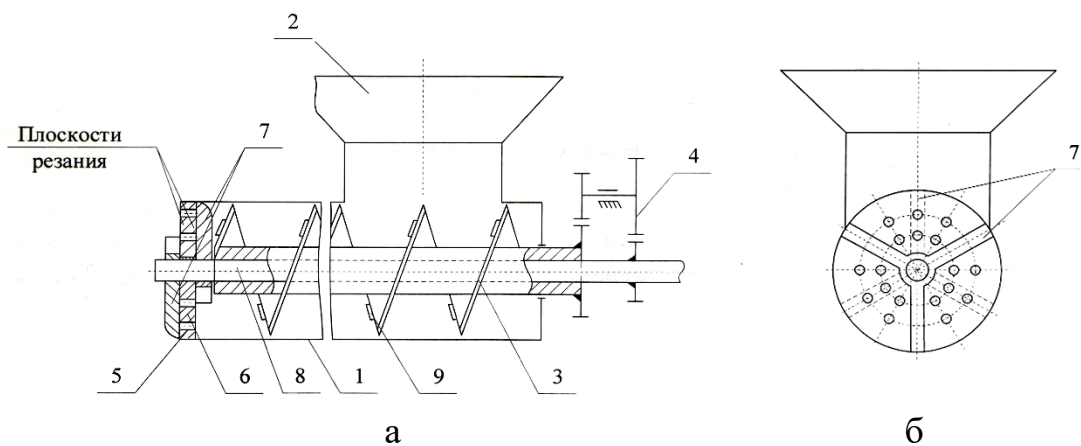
Схема измельчителя коры: а – вид спереди; б – вид слева
